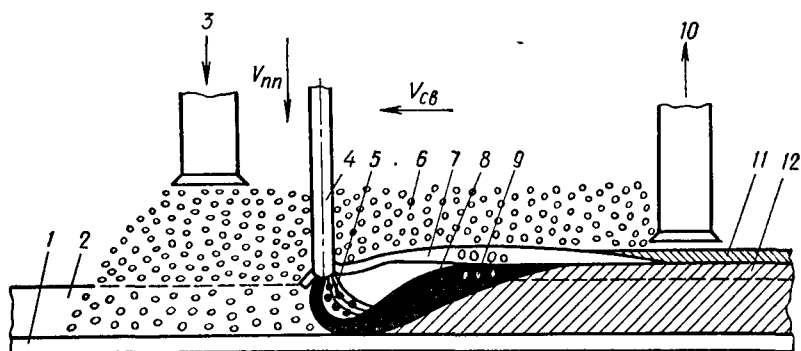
Схема процесса автоматической сварки под флюсом
